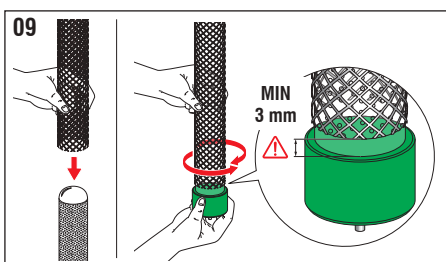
Riavvitare delicatamente il tubo ionizzante afferrandolo alla base (parte verde).
